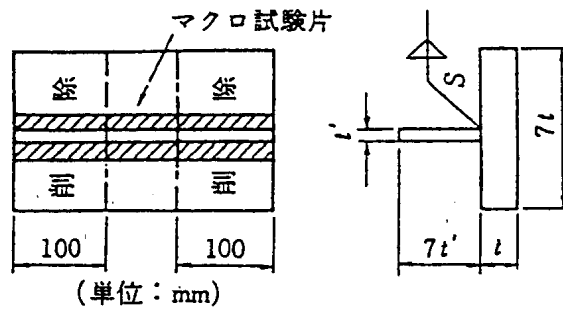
すみ肉溶接試験（マクロ試験）溶接方法及び試験片の形状
